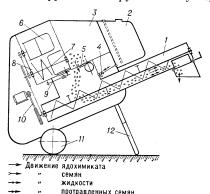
Шнековый протравливатель: 1— смесительный шнек; 2— резервуар для воды; 3— бункер для семян; 4, 5 и 9— дозитующие мергилисти. 9— дозирующие механизмы; 6— воро-шилка; 7— подающий механизм; 8—бун-кер ядохимикатов; 10— приводной ме-ханизм; 11— рама с колёсным ходом; 12— подставка.
